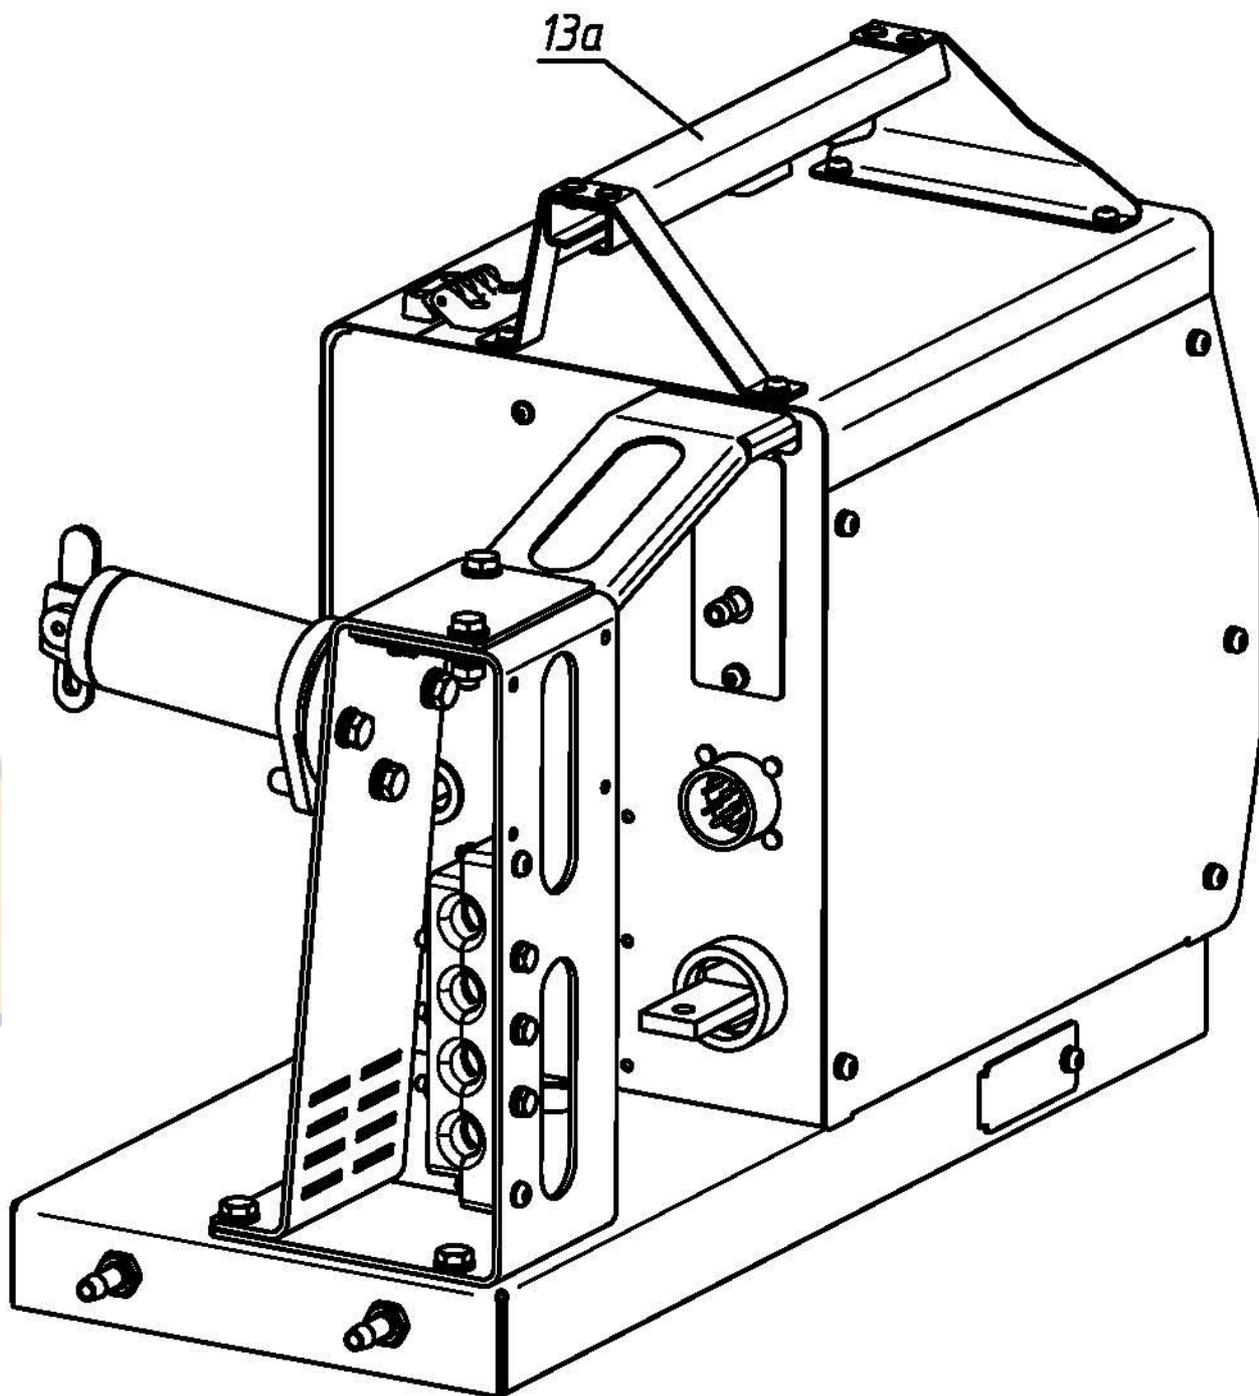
а (лист 2 из 2) – Внешний вид подающего механизма без металлической защитной рамы
